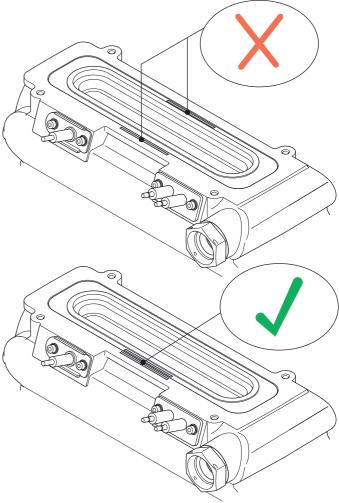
Lugar de montaje del quemador, superficie del quemador sobre cuerpo de caldera
